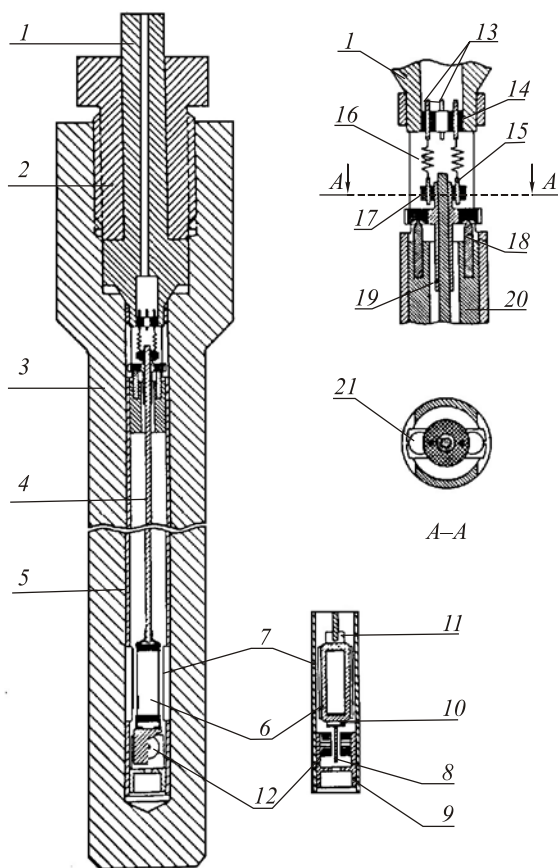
Маятниковые весы и камера высокого давления: 1 — головка; 2 — прижимной винт; 3 — корпус камеры; 4 — шток; 5 — корпус весов; 6 — компенсационная катушка; 7 — окна; 8 — лепесток датчика отклонения; 9 — обойма; 10, 11 — соединительные скобы; 12 — катушка датчика отклонения; 13, 15 — электрические переходники; 14, 17 — обоймы; 16 — пружинные токоподводы; 18 — иглы; 19 — насадка; 20 — опора для игл; 21 — подпятники.
